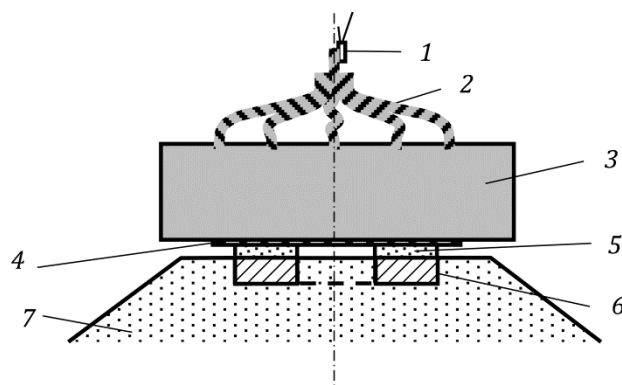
Схема нанесения покрытий на поверхности трения заготовок деталей осевых подшипников:
